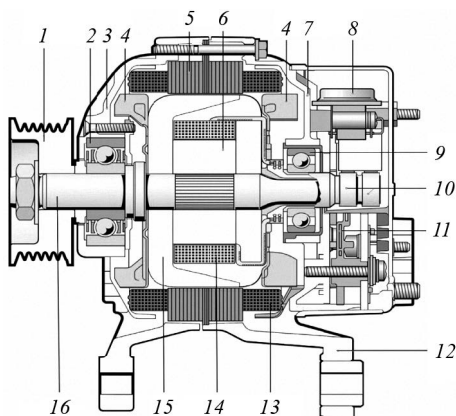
Генератор переменного тока компактный: 1 – шкив; 2 – передний подшипник; 3 – передняя крышка; 4 – вентилятор; 5 – статор с обмоткой; 6 – стальная втулка; 7 – задняя крышка; 8 – щеткодержатель с регулятором напряжения; 9 – задний подшипник; 10 – контактные кольца; 11 – выпрямительный блок; 12 – крепежная лапа; 13 – обмотка статора; 14 – обмотка возбуждения; 15 – клювообразный ротор; 16 – вал ротора
